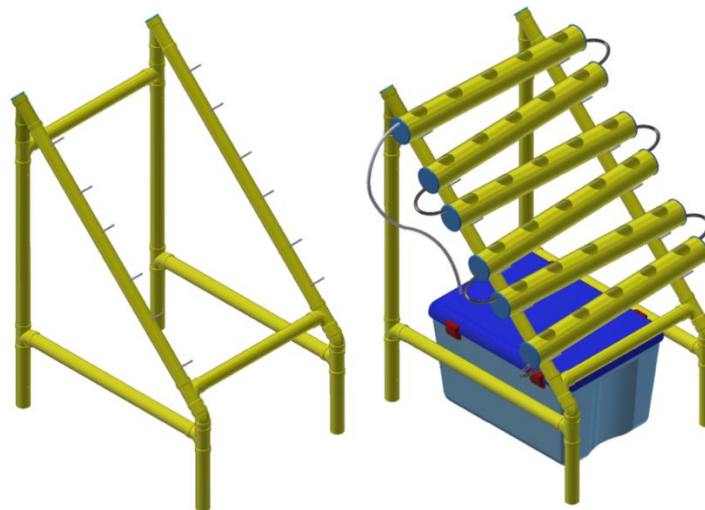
Planos en 3D del sistema NFT. Fuente: (Rosero, 2019)
